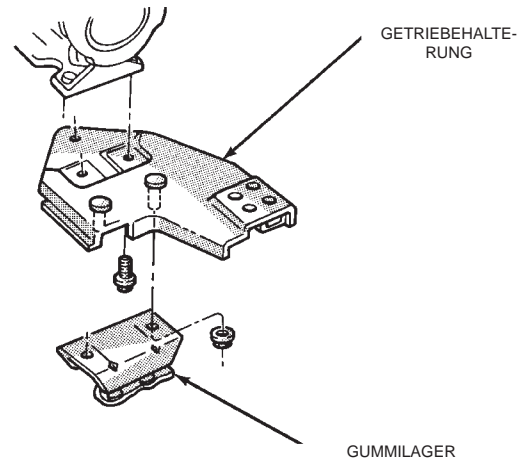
Hintere Aufhängung (Schaltgetriebe)
